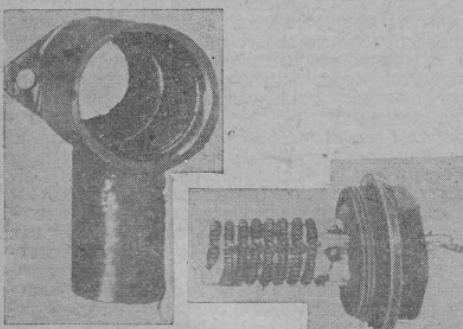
Нагревательный элемент. Слева — корпус грелки
